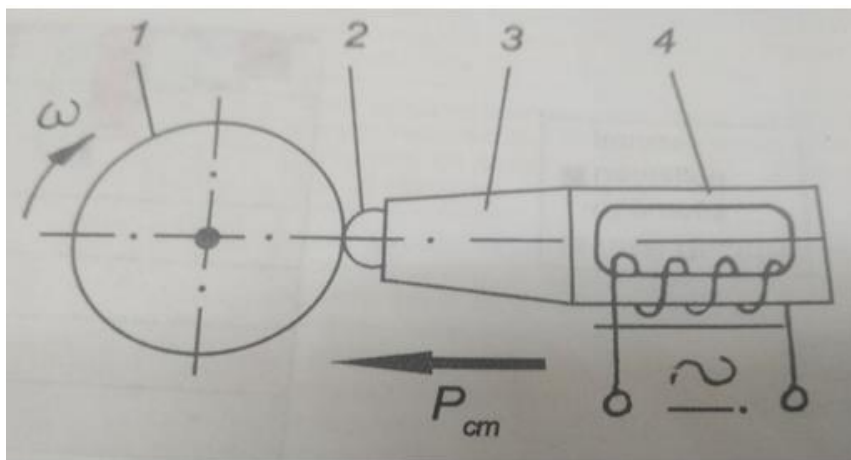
Схема ультразвукового зміцнення поверхні валу:
